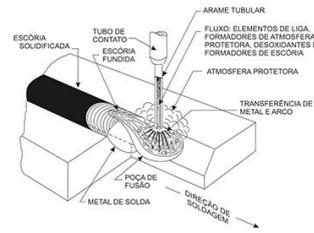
Diagrama soldagem com arames tubulares autoprotégidos
